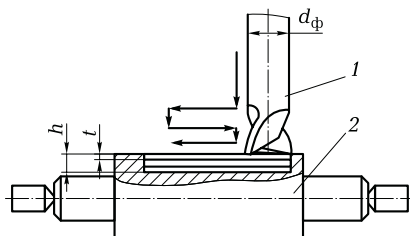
Схема фрезерования шпоночного паза на специальном шпоночно-фрезерном станке:
